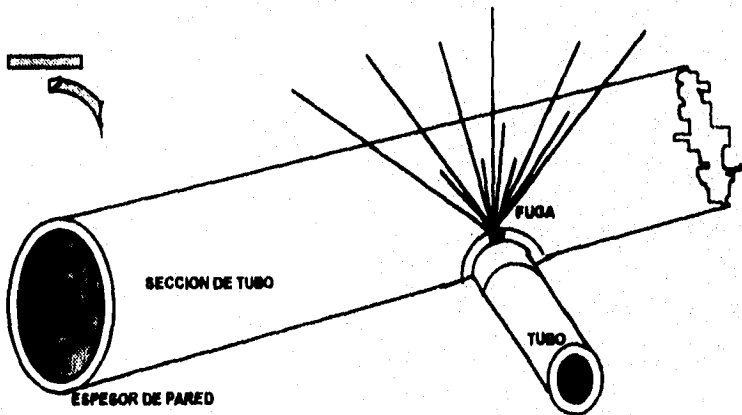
k) Rotura en, o adyacente a soldaduras de conexiones o elementos de refuerzo.
